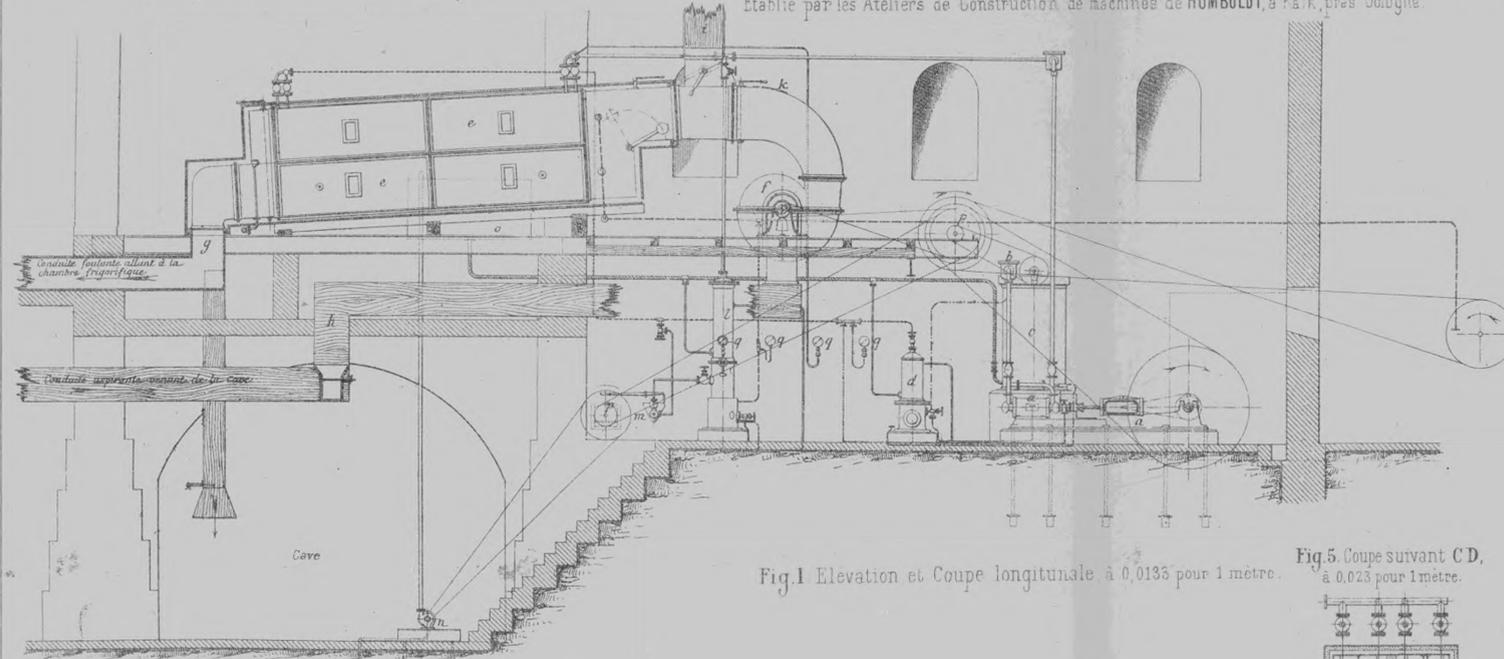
Elevation et Coupe longitudinale à 0,0133 pour 1 mètre.
